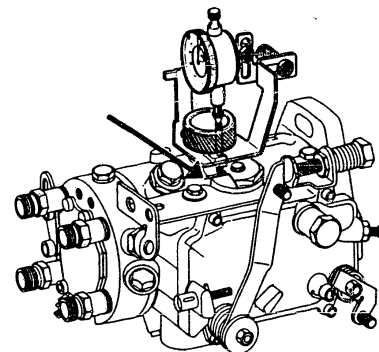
Einstellrille (Pfeil) an der Roto-Diesel-pumpe.
